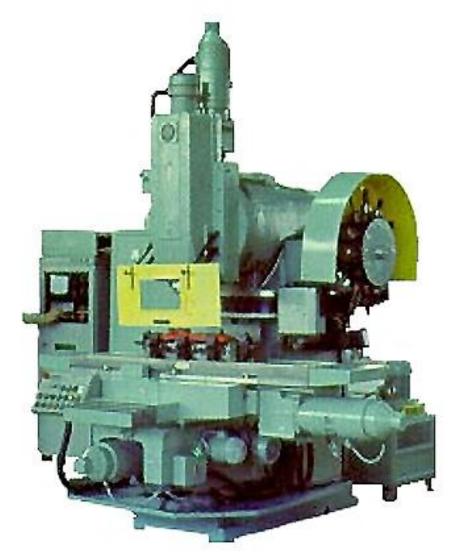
Вертикальный станок с магазином типа «РУКА» и диском с инструментами
